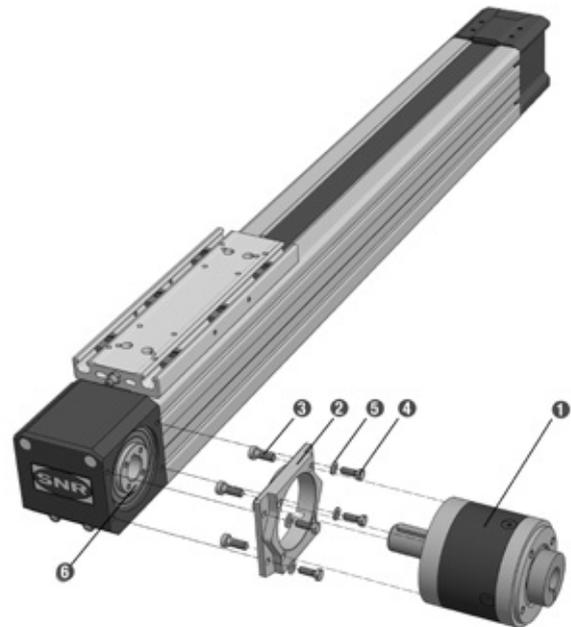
Montage rapporté de réducteurs planétaires sur un module linéaire à entraînement par courroie dentée
